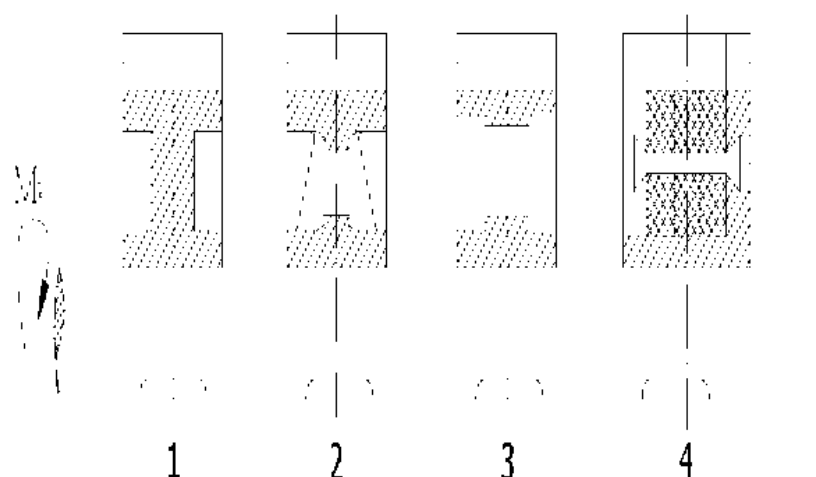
1 – стальные кованные, 2 – литые из серого чугуна, 3 – сварные, 4 – составные из пластмасс.
